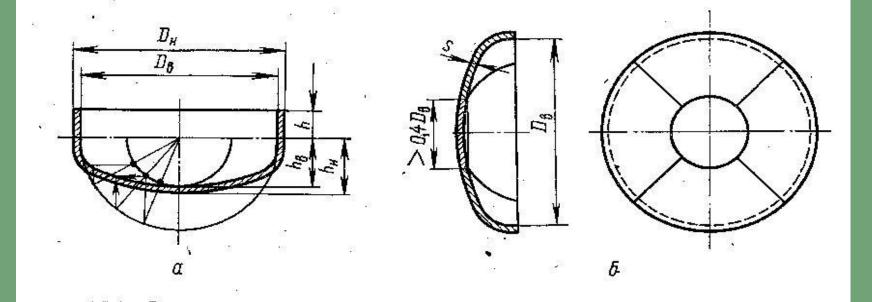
Эллиптическое днище: а-цельноштампованное; б- сварное из сегментов и лепестков
